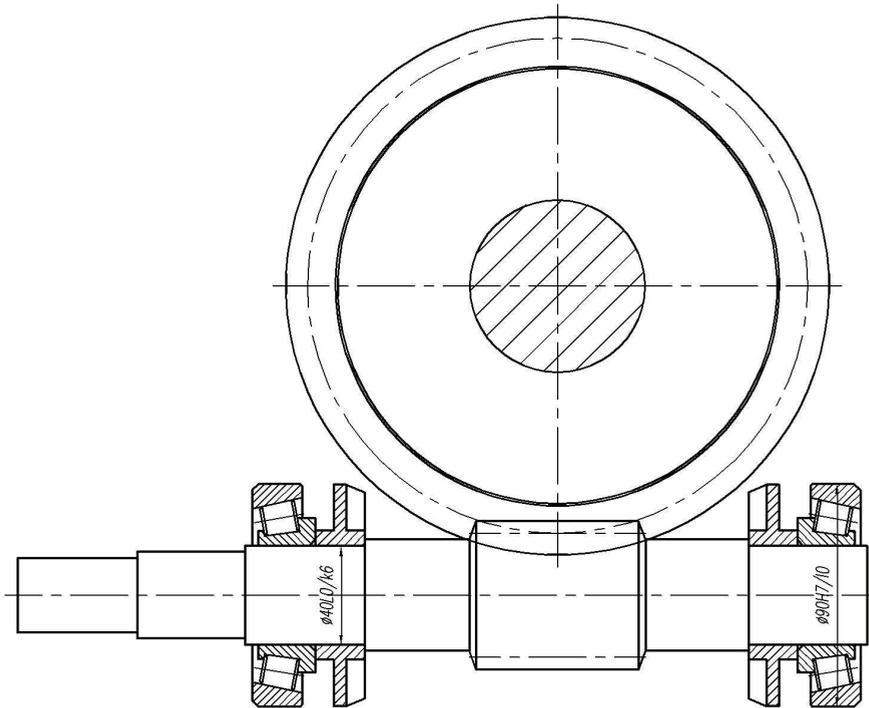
Корректировка длин участков IV и VI вала червяка
